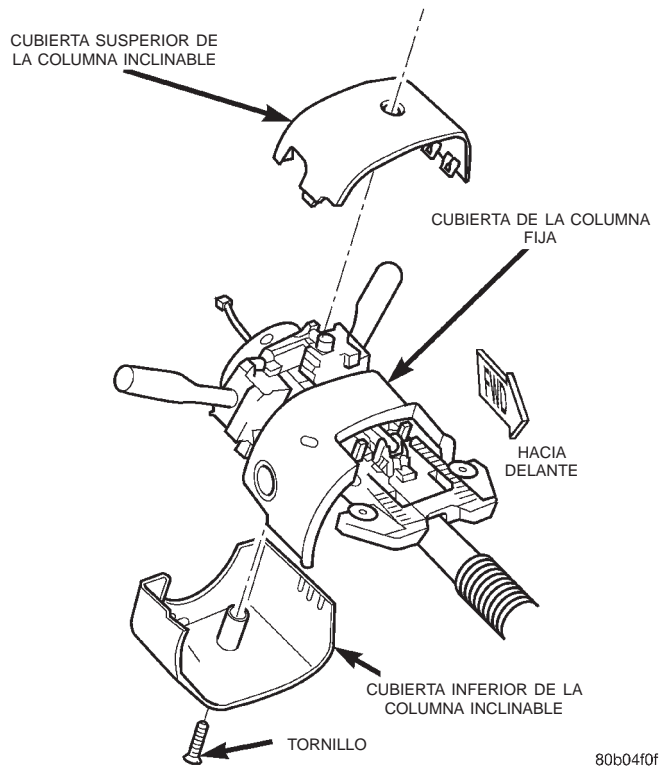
Desmontaje e instalación de las cubiertas de la columna de dirección
